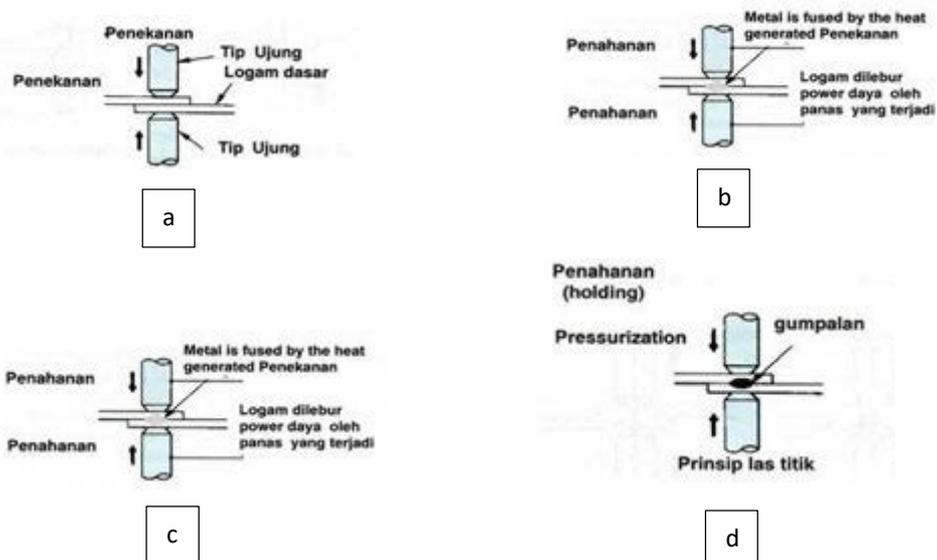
Resistance Spot Welding (RSW)
